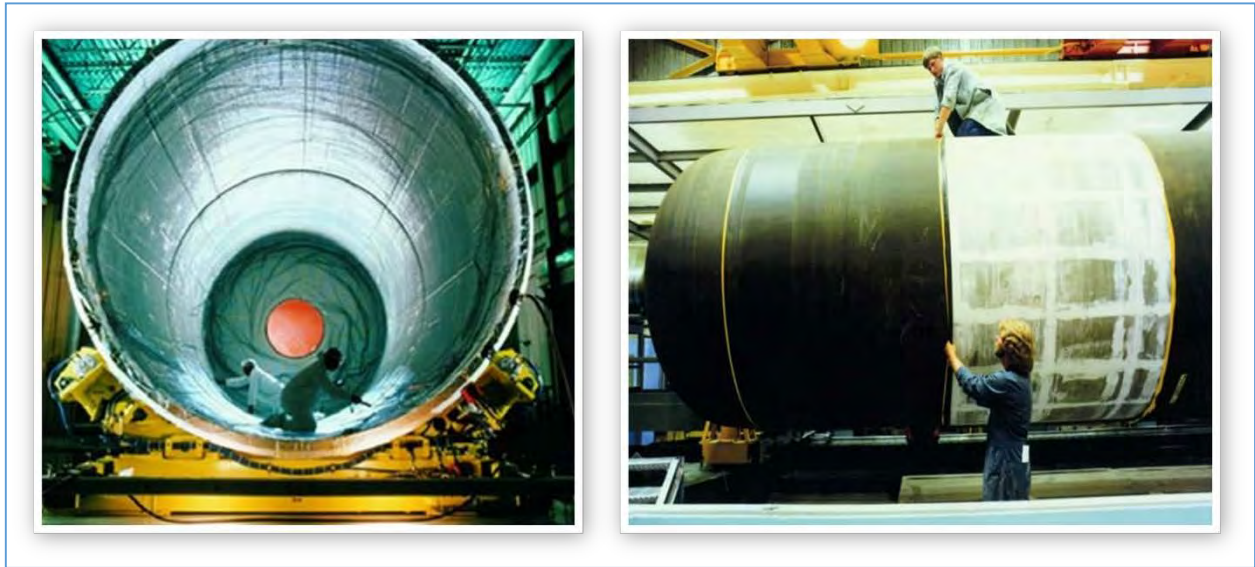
Izquierda:* Instalación de aislamiento dentro de una carcasa de motor de cohete de filamentos bobinados. (Thiokol Corp.)
